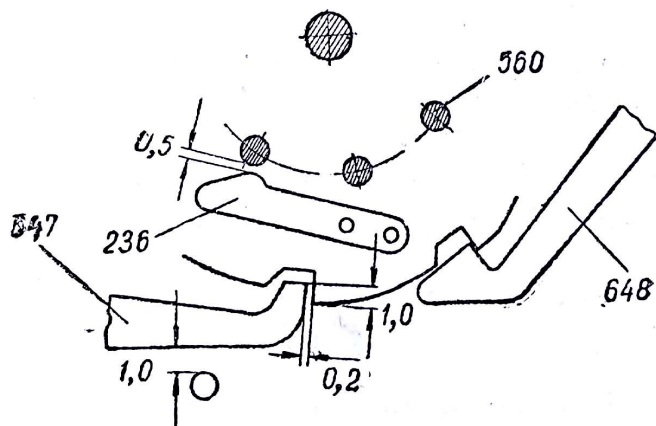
Регулировка деталей механизма транспорта барабанов.
